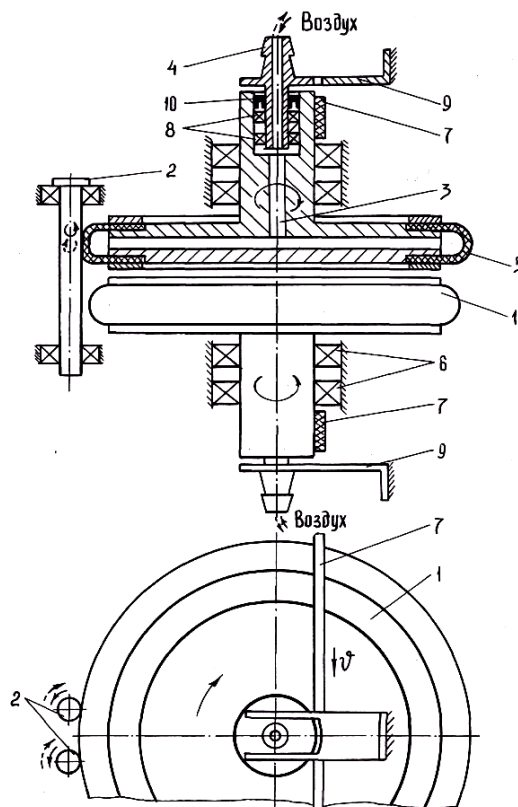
Схема механизма привода реверсивных вьюрков пневмомеханическими дисками
